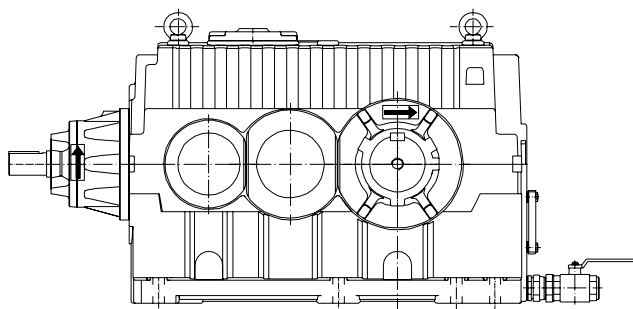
Разрешенное направление вращения показывается на корпусе зубчатого механизма.
